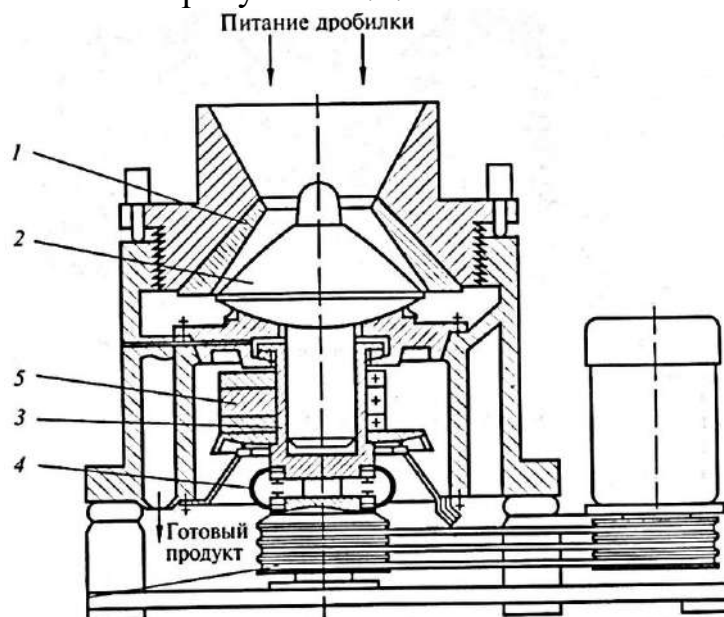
Принципиальная схема и общий вид промышленной дробилки КИД: 1 – цилиндрическая чаша; 2 – дробящий конус; 3 – вал; 4 – гибкая трансмиссия; 5 – дебалансный вибратор
